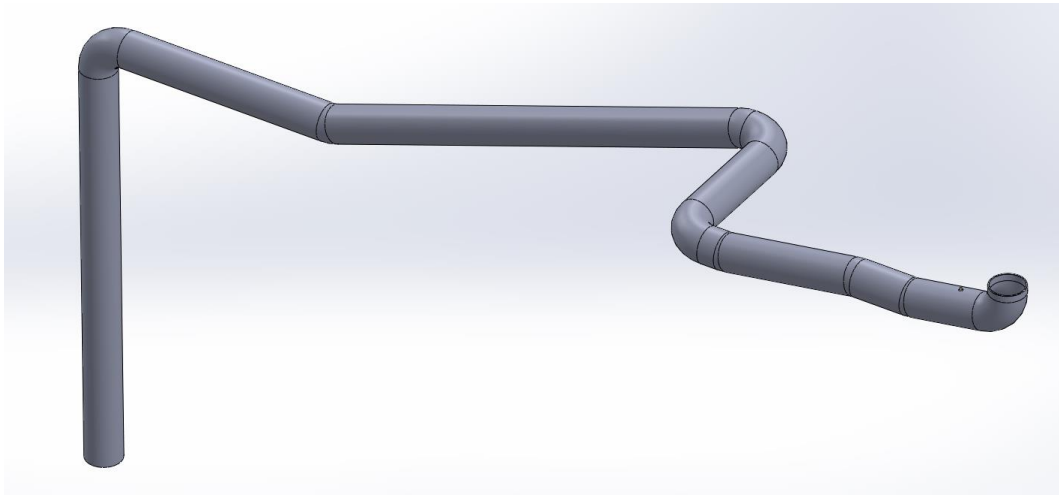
Sub-ensamblaje 01-11-00, respectivo a la Tubería de Desagüe del cilindro principal de la máquina de vapor de Newcomen. Vista general completa.
